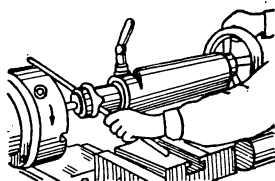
Направление плашки с помощью пиноли задней бабки.
